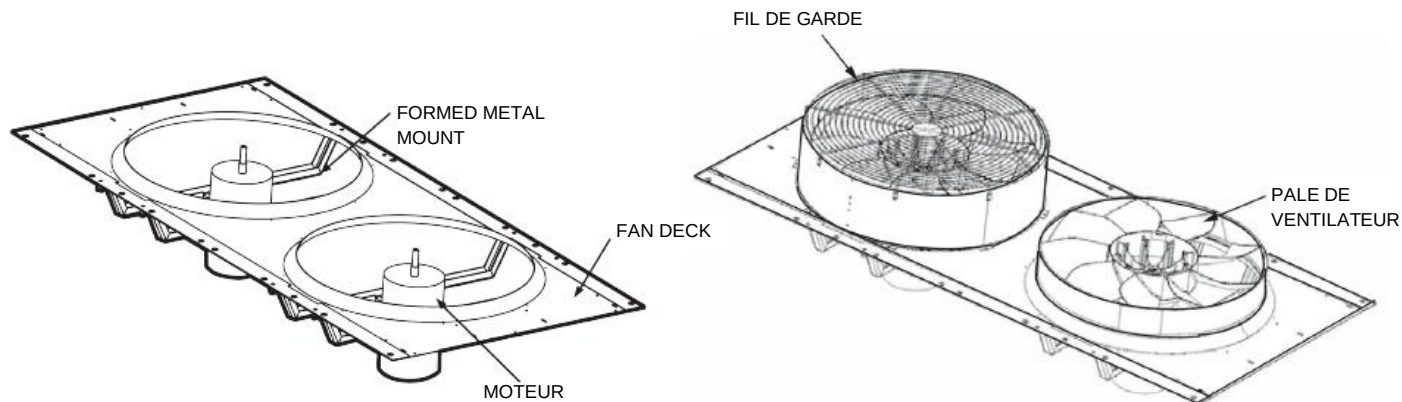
Montage du Moteur et des Pales du Ventilateur
